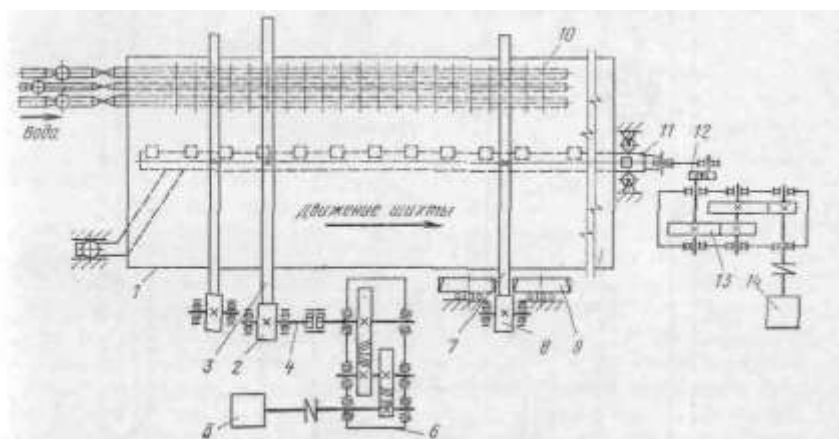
Кинематическая сема привода барабанного смесителя
